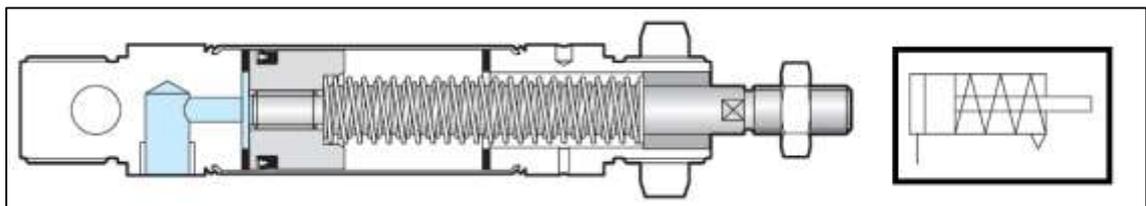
Cilindro de simple efecto – Dibujo en sección y símbolo.
